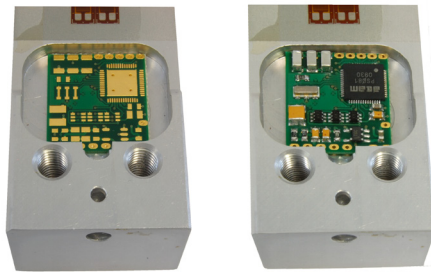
未装配/装配元件的 PCB 放入传感器预留的位置中
